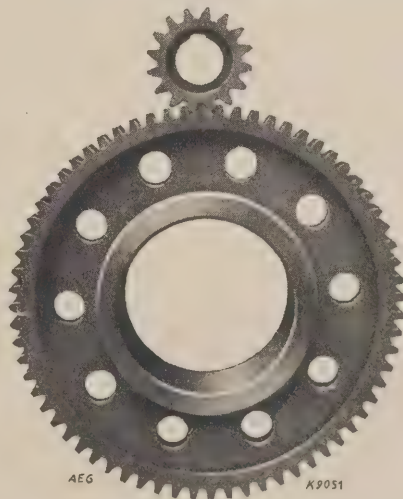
Zahnräder zum Bahnmotor GBM 700.
